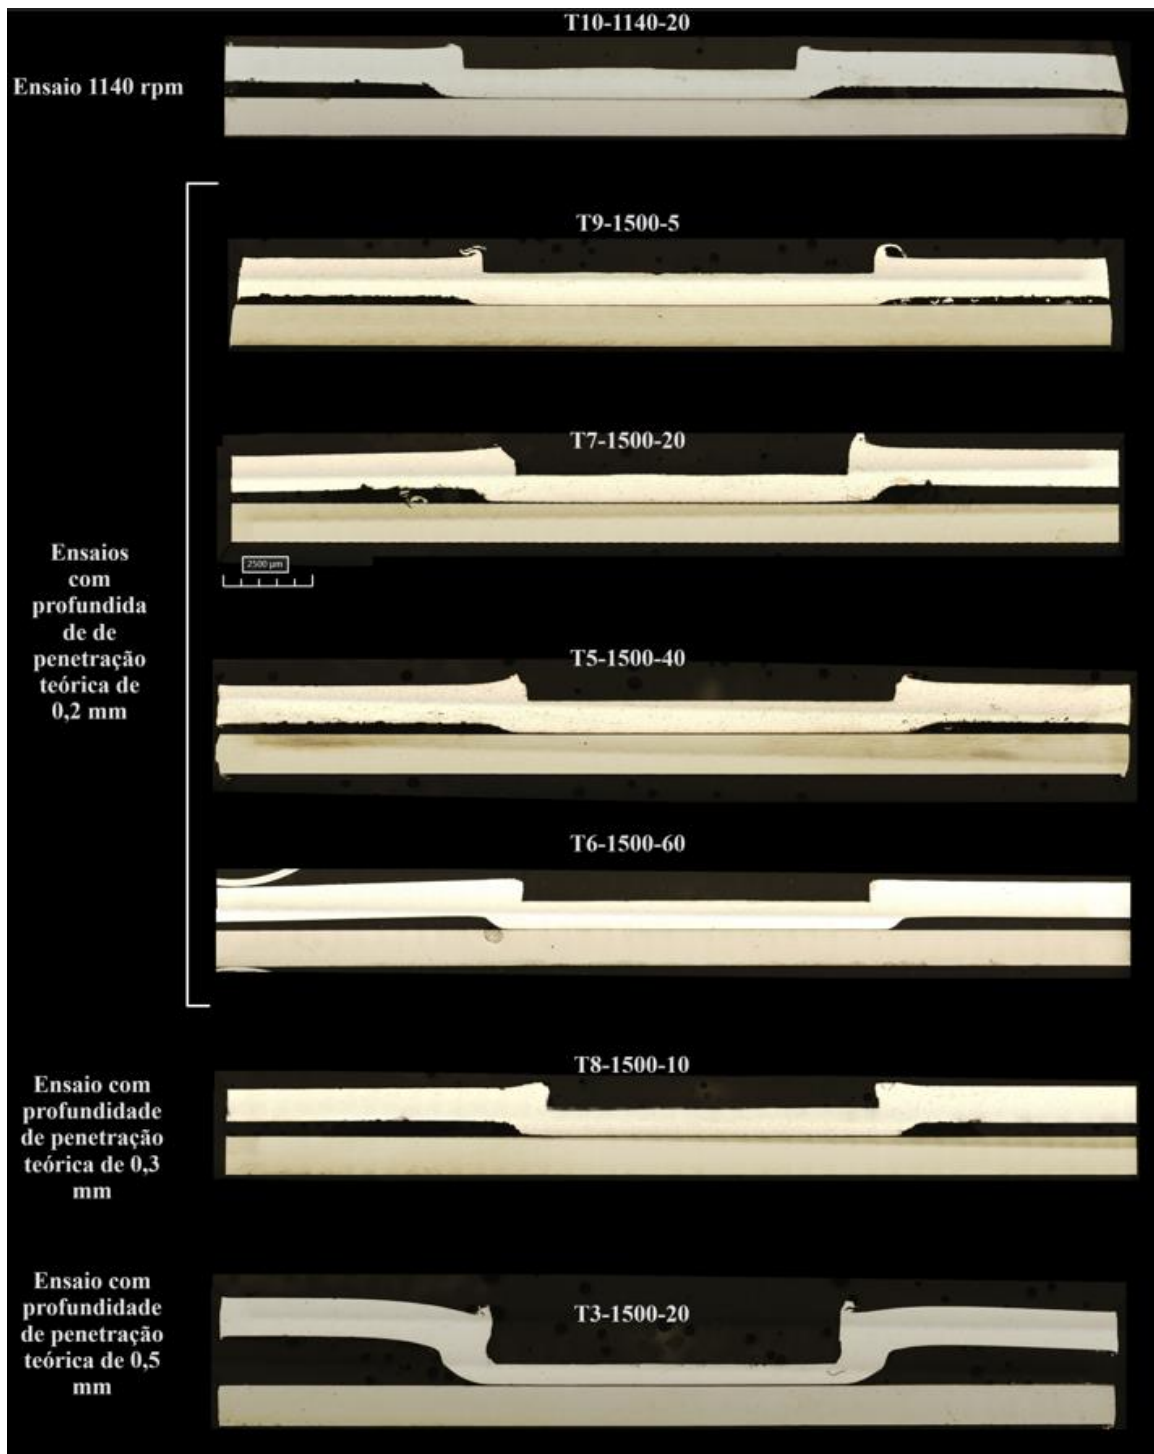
Macroestruturas das soldaduras analisadas.
